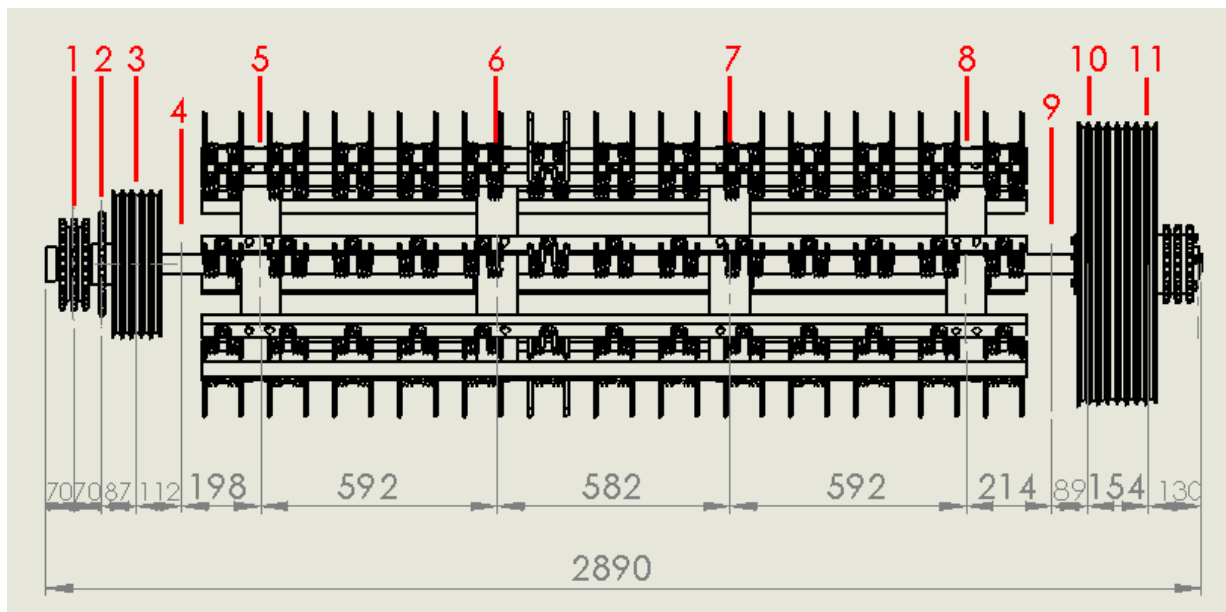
Vista frontal de elementos principales de segundo cilindro
